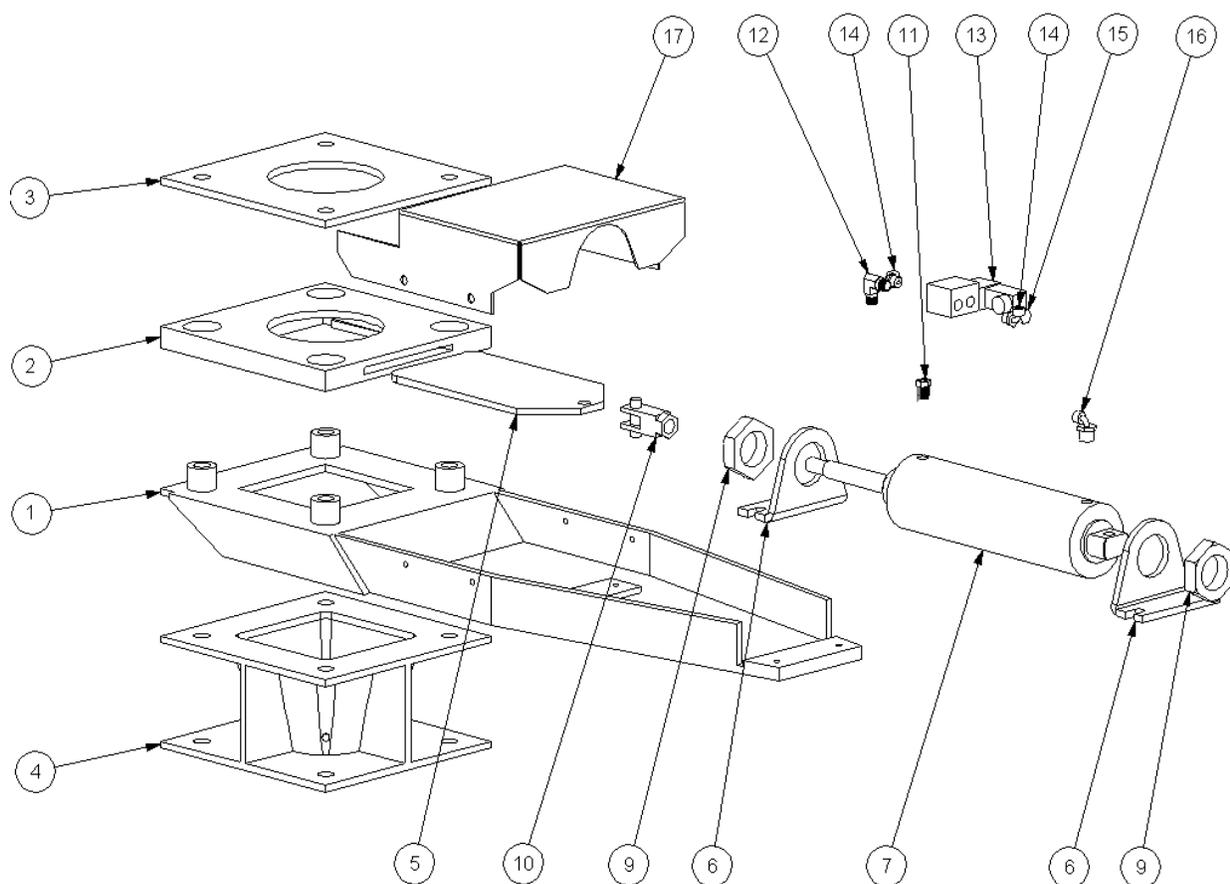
Lista de partes del ensamble típico de puerta de cuchilla (debajo de la mezcladora)
